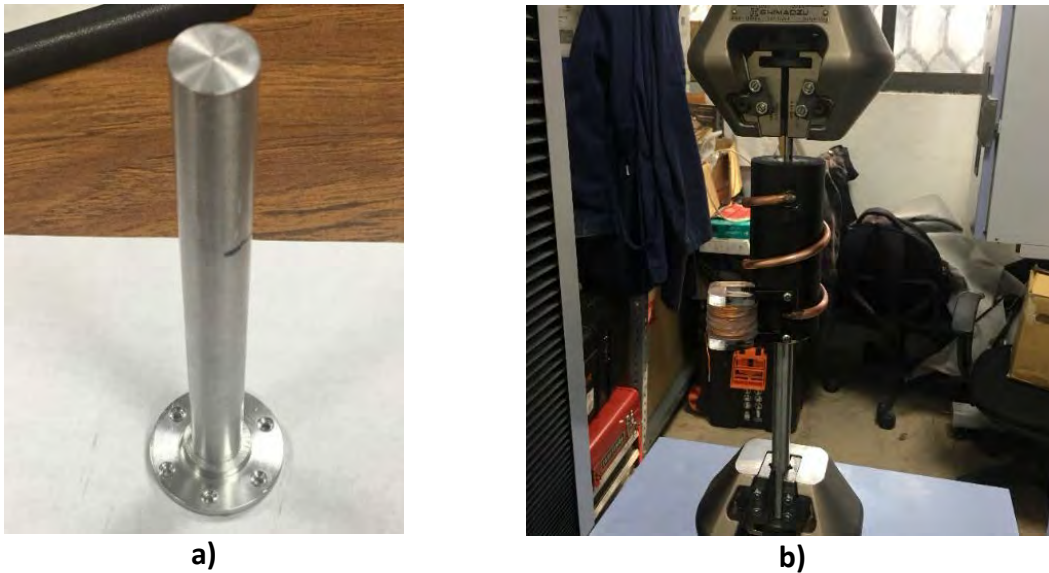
a) Aditamento mecánico de sujeción, b) montaje del inersor MR.
